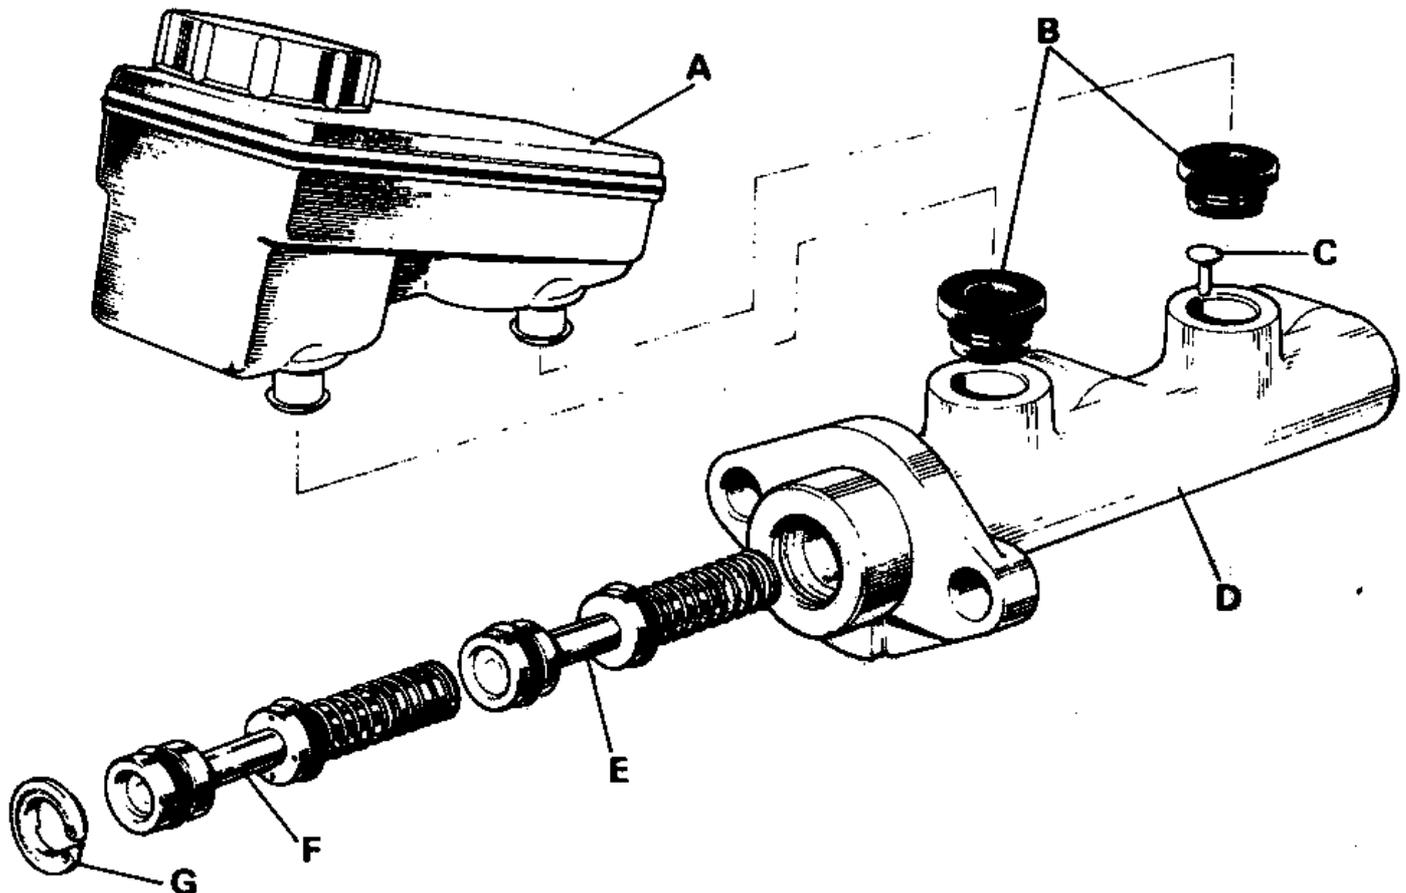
Главный тормозной цилиндр (Разд. 15)
